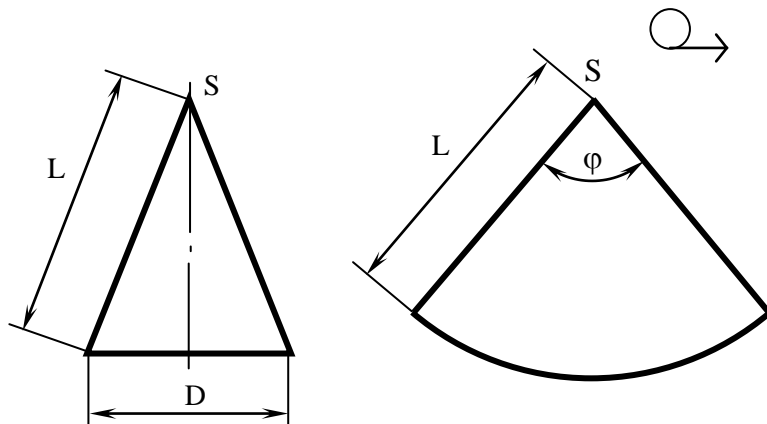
Построение развертки боковой поверхности прямого кругового конуса
